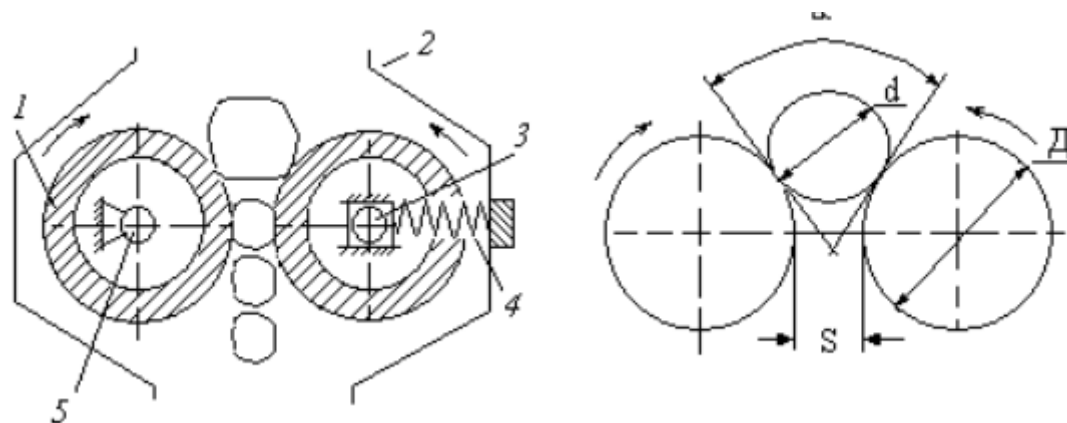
Схема духвалковой дробилки : 1 – валок; 2 – корпус; 3 – подвижный подшипник; 4 – предохранительная пружина; 5 – неподвижный подшипник
